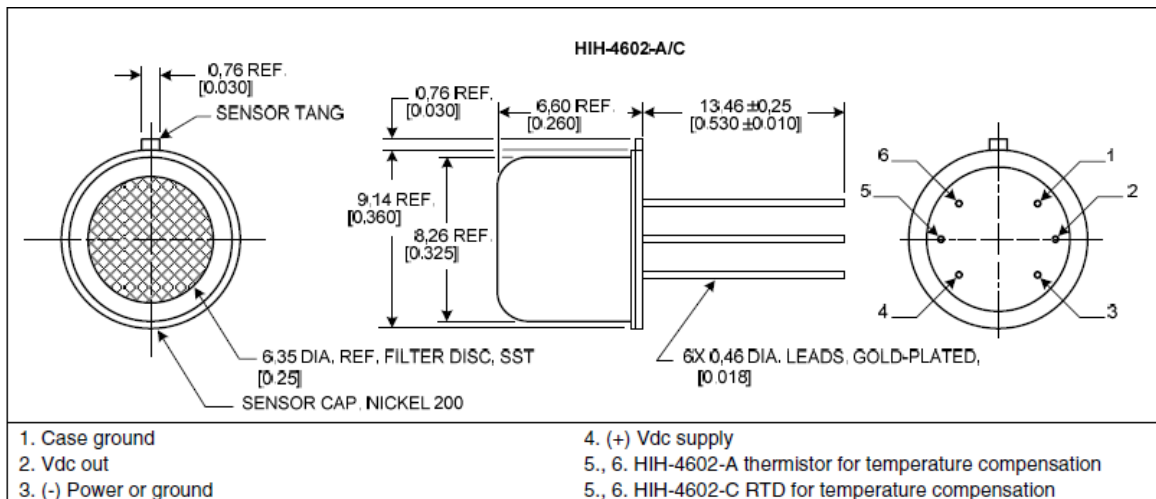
Dimensiones de montaje del sensor HIH-4602-A/C Series en mm [in] [63].
